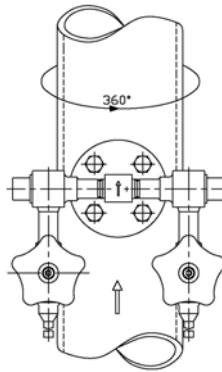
Installation in einer vertikalen Rohrleitung Typ: IBFD-25...-K7-A18
